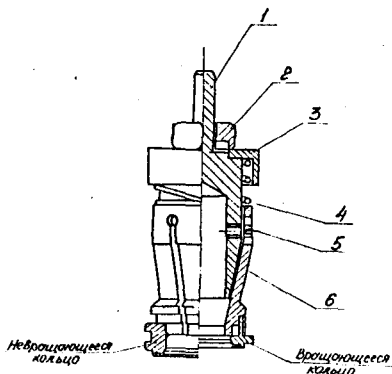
Приспособление для снятия фасок: 1 – сердечник; 2 – гайка; 3 – упор; 4 – пружина; 5 – стопорный винт; 6 – цапга.
